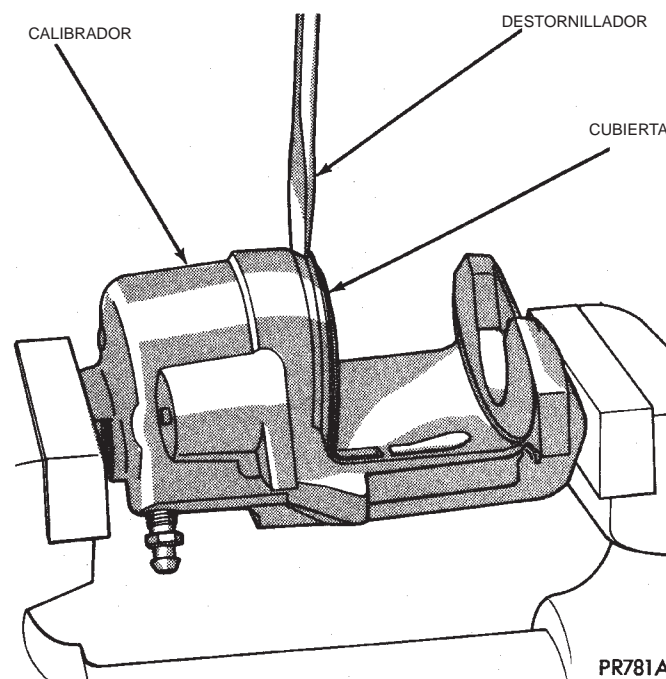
Desmontaje del calibrador/cubierta guardapolvo del pistón
